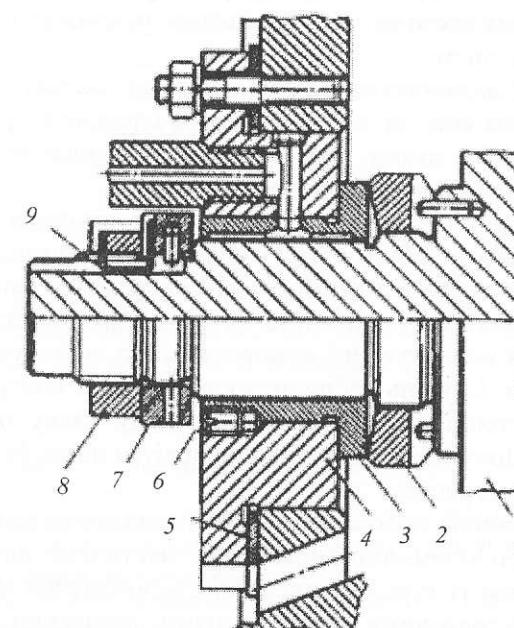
Конструктивна схема опорно-упорного підшипника ротора турбокомпресора:
